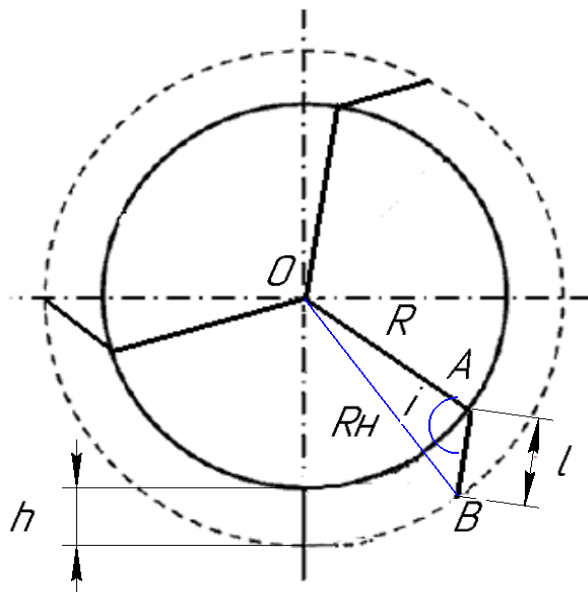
Расчетная схема для определения угла установки ножа фрезы
